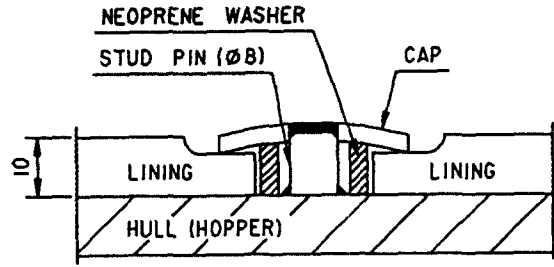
Typical Section of Fastening Element (Lining 표면에 Flush 하게 설치)
